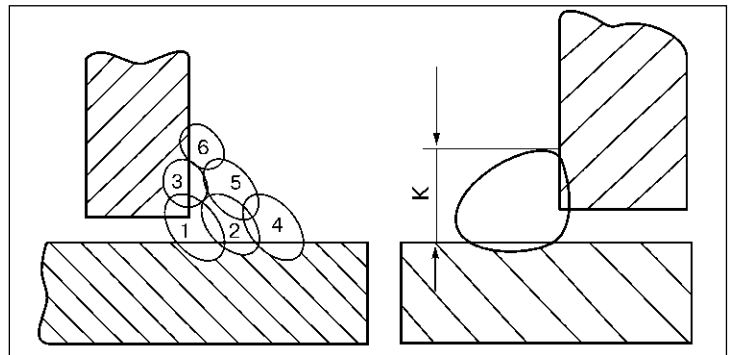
Выполнение угловых швов ручной дуговой сваркой без разделки кромок: а — многопроходная сварка (1–6 — последовательность проходов); б — однопроходная сварка (к — катет шва)
